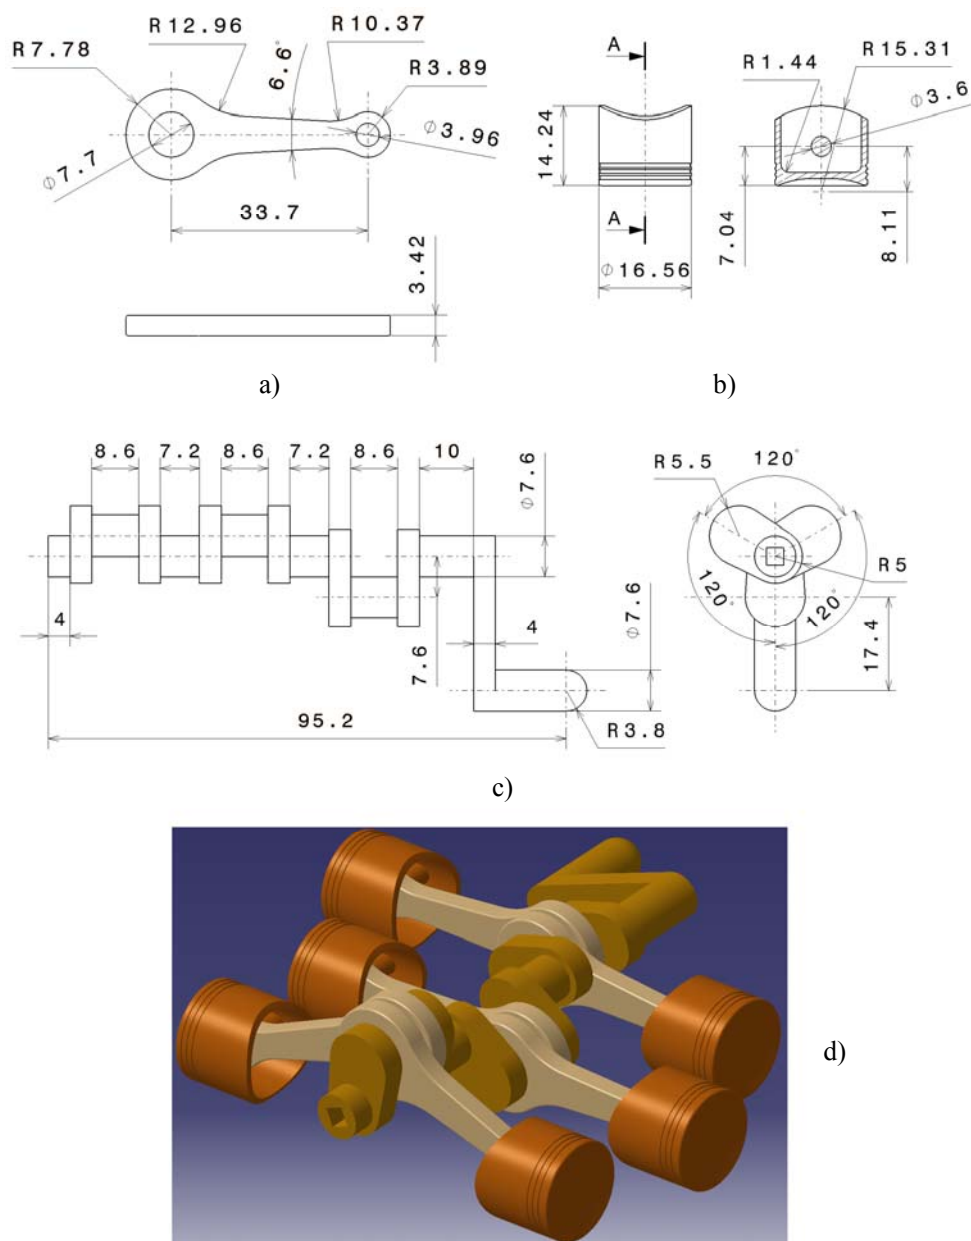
Dimensiunile bielei (a). Dimensiunile capului de piston (b). Dimensiunile arborelui cotit (c). Modelul 3D al ansamblului (d)
